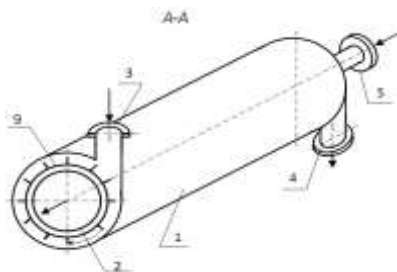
Аксонометрический вид теплообменника с устройством для очистки наружной поверхности труб в разрезе
